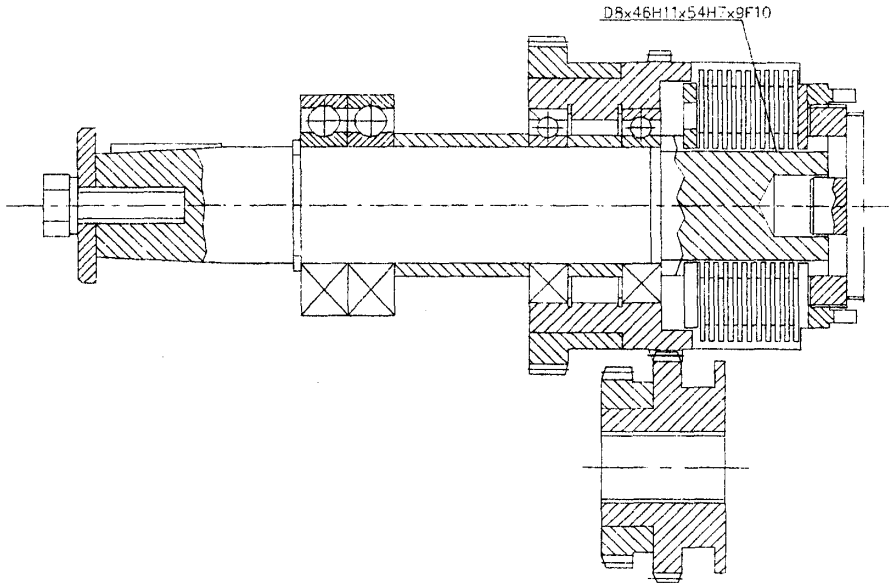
Конструктивна схема зубчастої передачі від вала I до вала II
